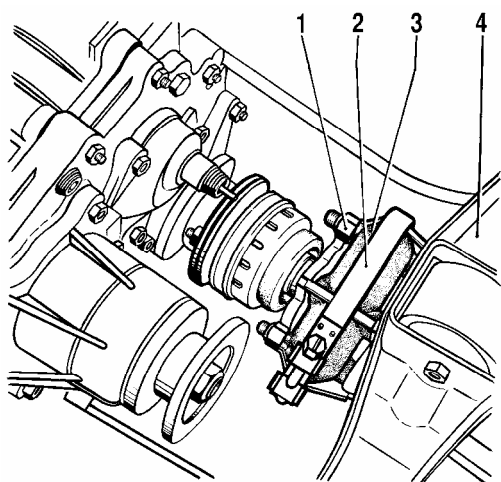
Эластичная муфта соединения карданного вала с коробкой передач:
